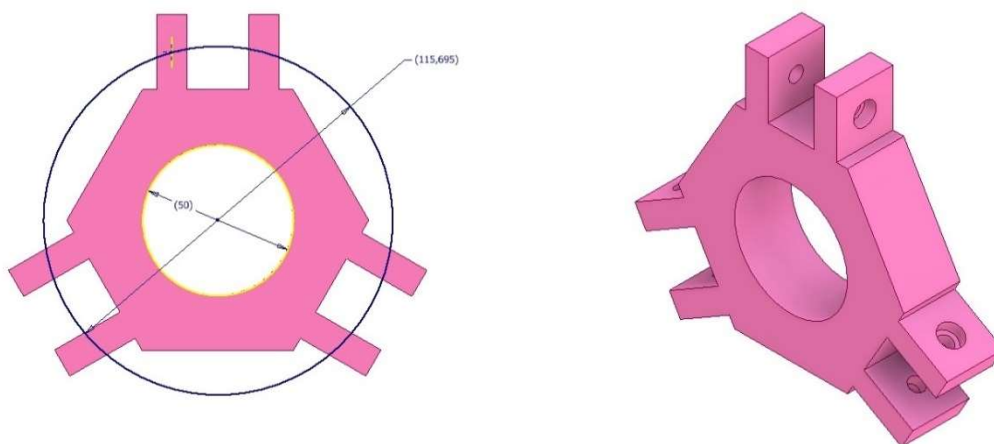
Kritické místo pro splnění požadavku elevace 90 stupňů
